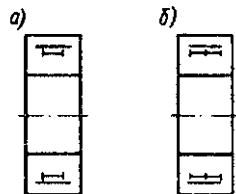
Игольчатый подшипник радиальный: *a* — однорядный; *b* — двухрядный
